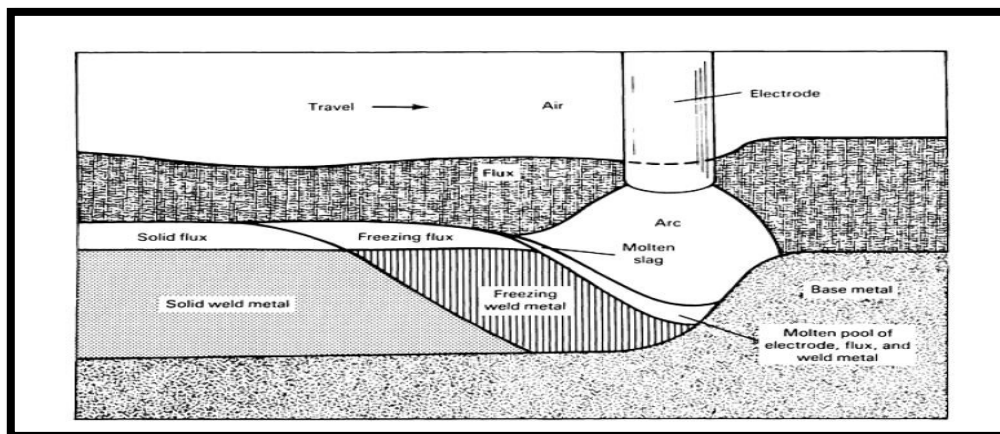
proceso de SAW. Soldadura protegida por el manto granular.
